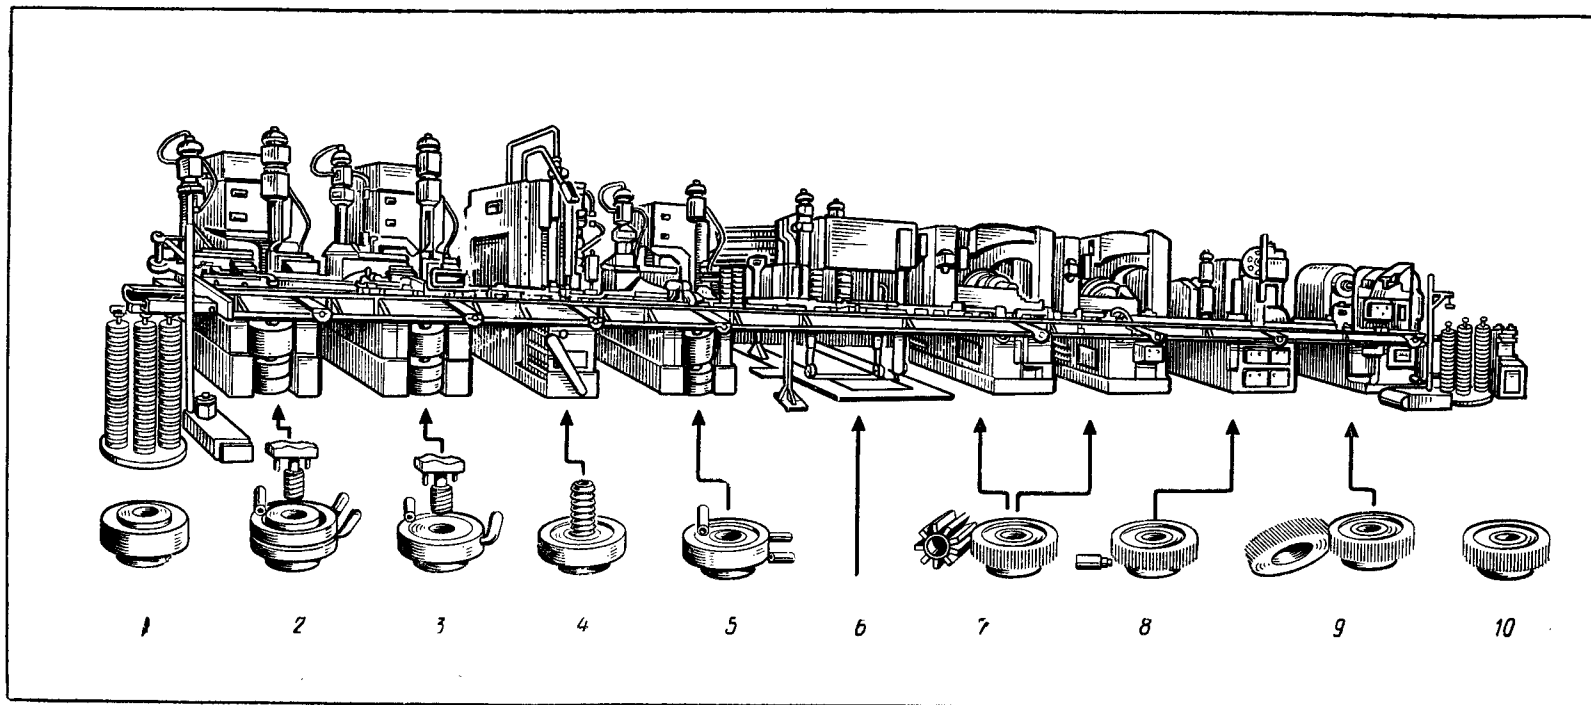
Автоматическая линия для обработки однозубчатых зубчатых колес:
